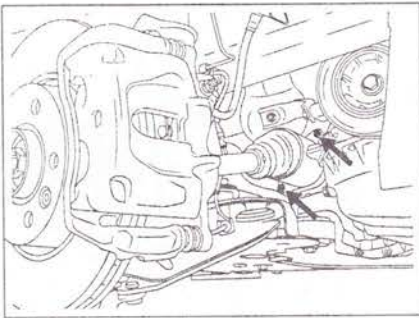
Открутите два болта крепления А промежуточной опоры и снимите промежуточную опору с кронштейна двигателя.
